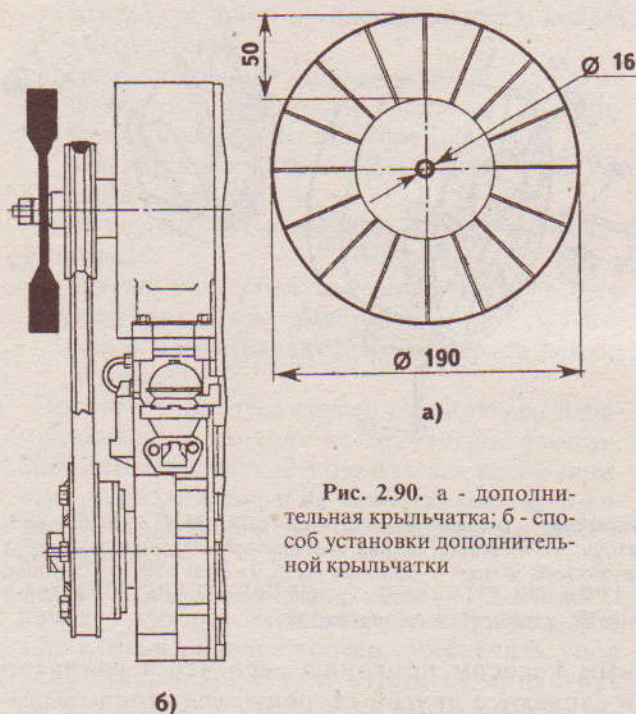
а - дополнительная крыльчатка; б - способ установки дополнительной крыльчатки
